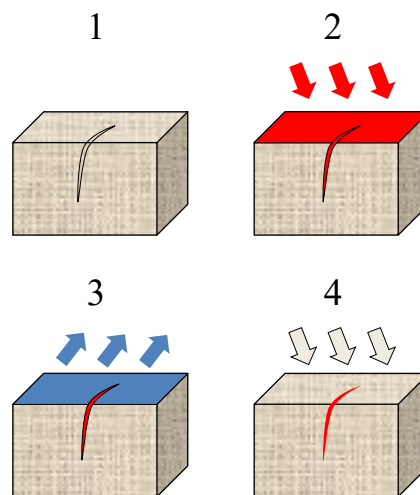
1) secção do material com uma fenda na superfície que não é visível a olho nu, 2) aplicação do líquido penetrante na superfície, 3) o excesso é removido, 4) aplicação do revelador que torna a fenda visível [adaptado de [6]]
